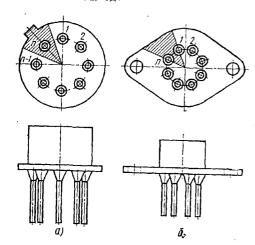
Конструкции корпусов типа 3 подтипов 31(a) и 32(b) с выводами круглого сечения
